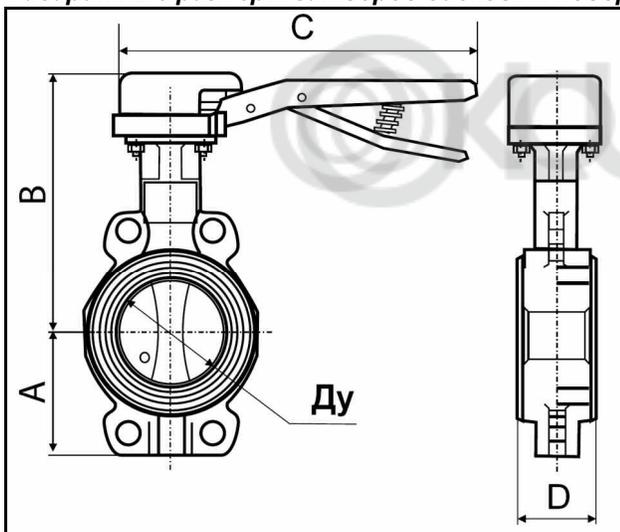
Габаритные и присоединительные размеры затворов дисковых поворотных типа VFY- WH с центрирующими проушинами
